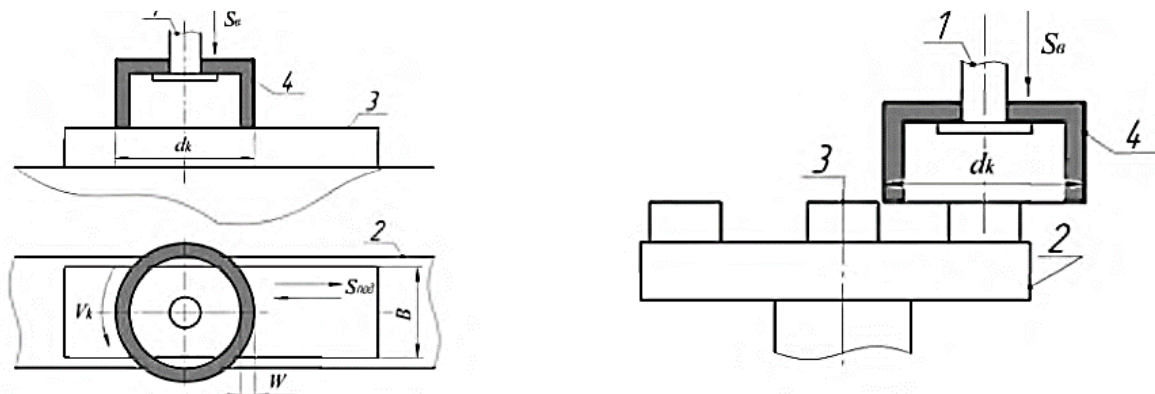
Основные схемы плоского торцевого шлифования: 1 – шпиндель; 2 – стол станка; 3 – заготовка; 4 – шлифовальный круг
